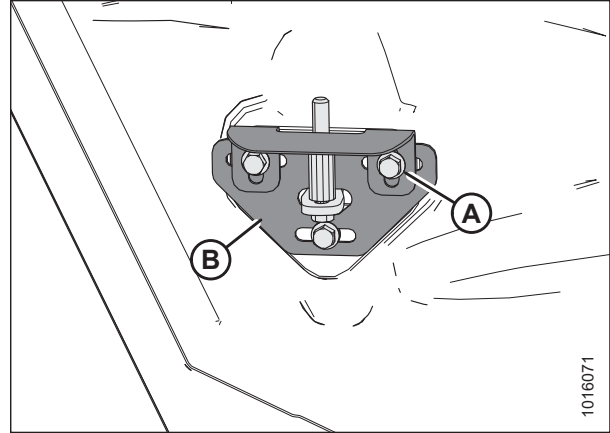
Засувка лівого бокового щитка в зборі
